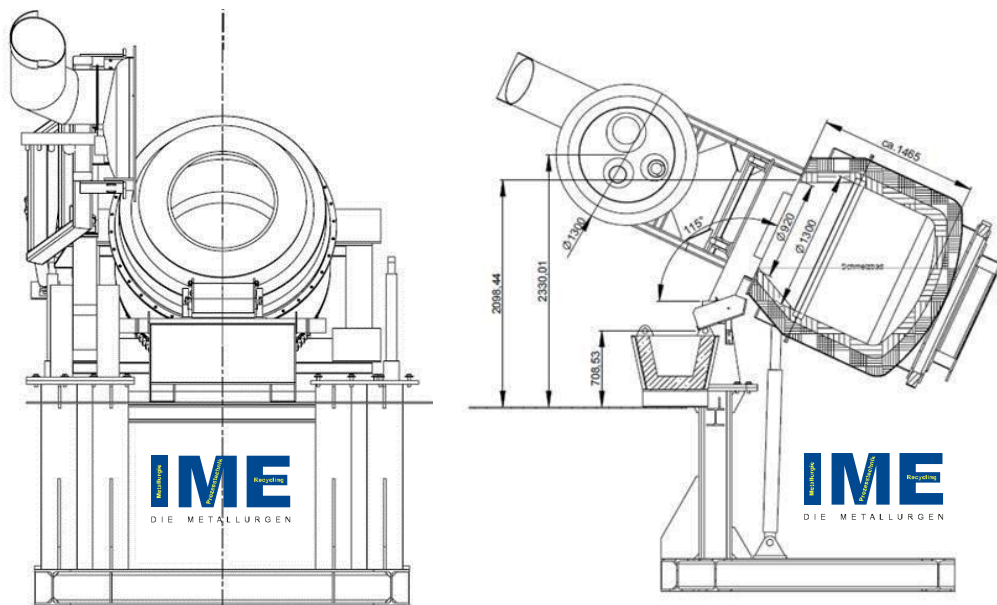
Schematische Ansicht des Aachener TBRCs inkl. Gießschnauze und -pfanne. Seitenansicht (links) und Frontansicht (rechts)
